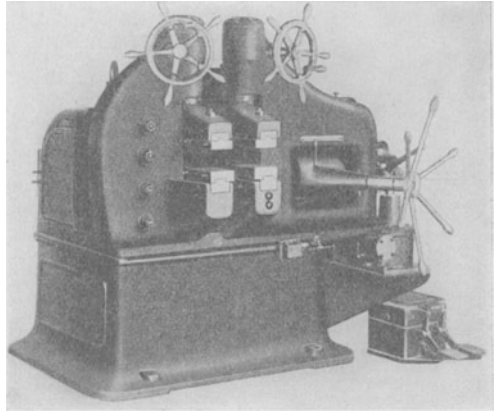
Größere Stumpfschweißmaschine.
